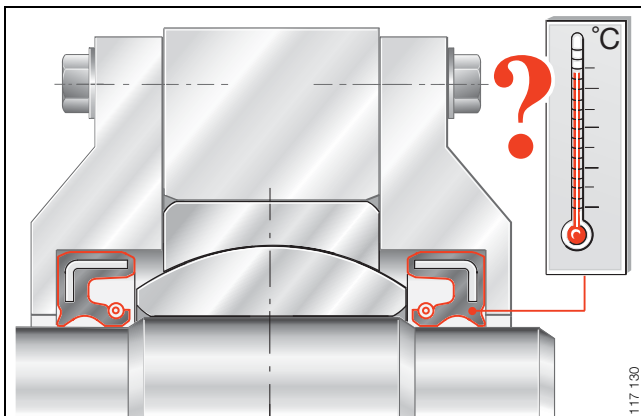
· Rotule sans étanchéité, étanchéités extérieures
